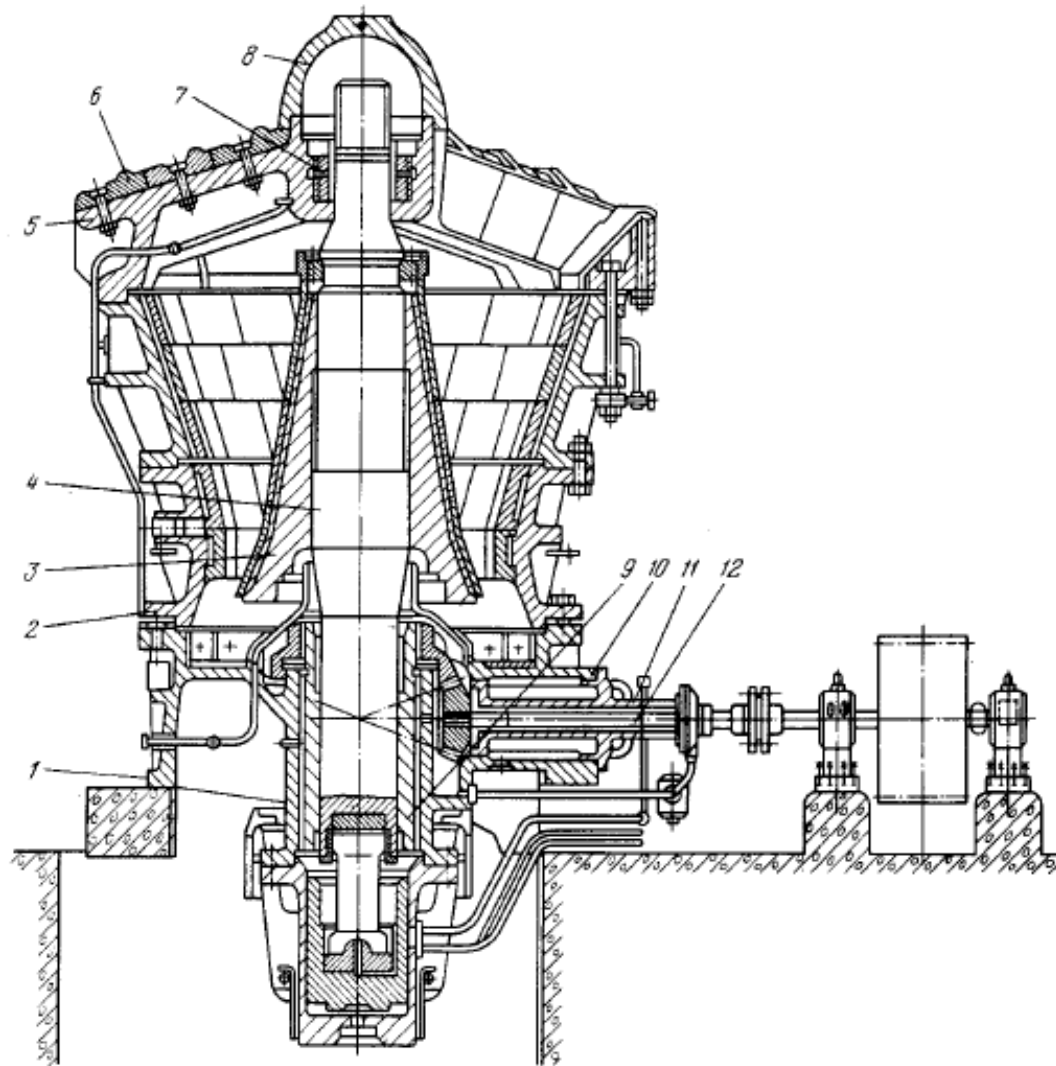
Принципова схема конусної дробарки крупного дроблення:
